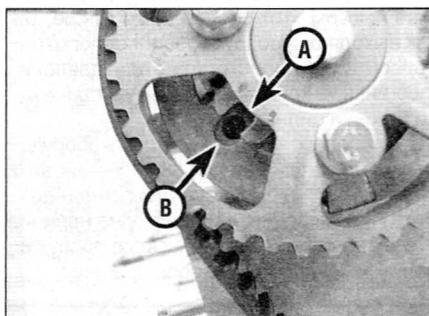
, б. Установочный паз (А) в ступице зубчатого шкива распределительного вала, совмещенный с установочным отверстием (В) в головке цилиндров (двигатели 2.0 л)
